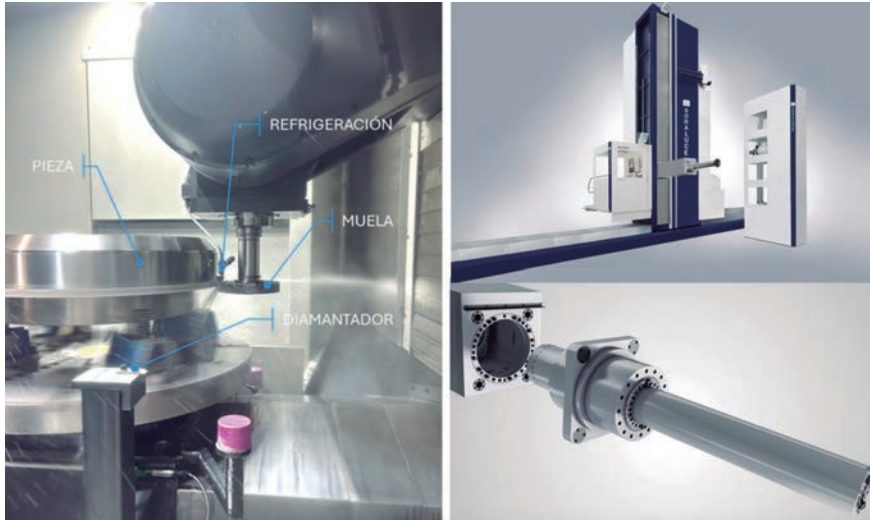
Máquinas multitasking: Izda. La máquina de Ibarma® THR16 con sistema de rectificado añadido en CFAA en 2024. Dcha. Fresadora-mandrinadora de Soraluze® FRX-16000 y sistema de mandrinado insertable en el cabezal.
